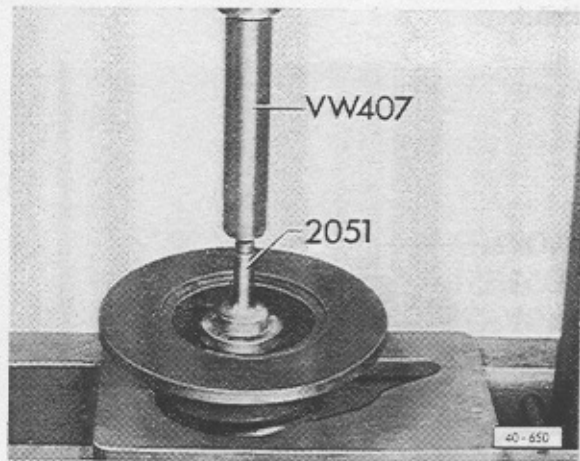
Dichtring eindrücken oder eintreiben (bündig)
